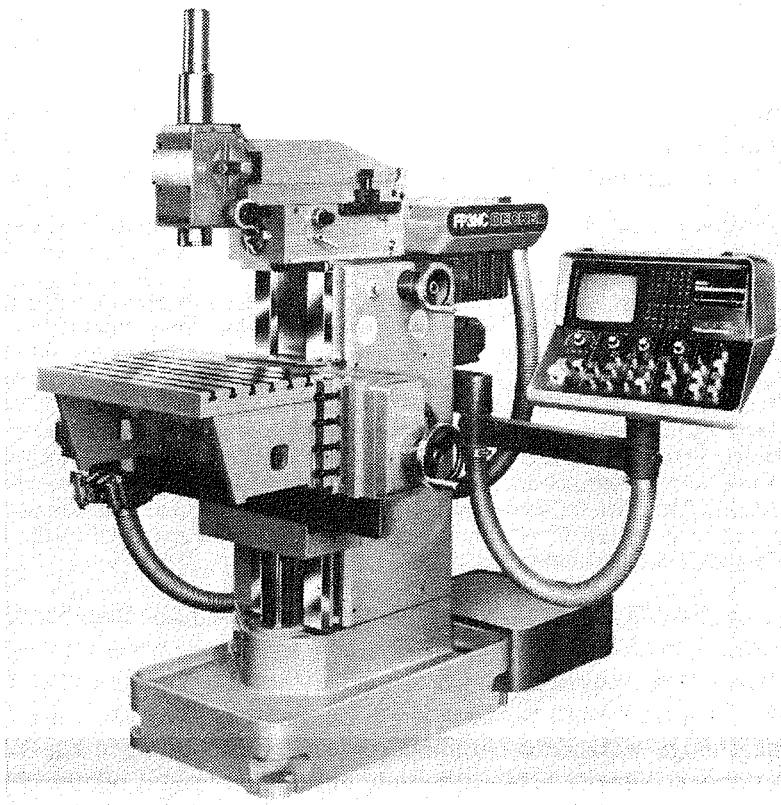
Universalfräsmaschine mit Handeingabesteuerung; erste Hälfte der 80er Jahre
